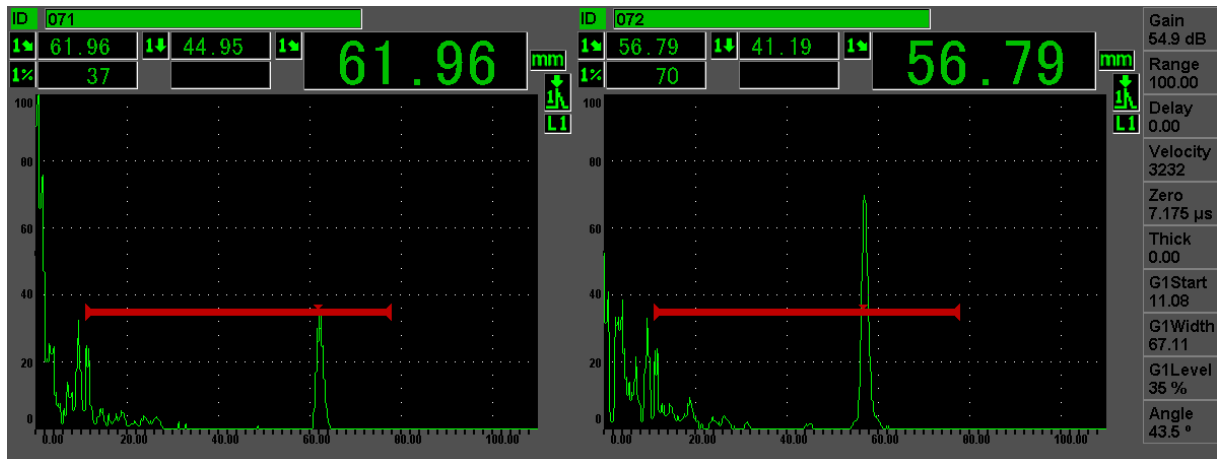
Rozdíly UT rovné a šikmé drážky
